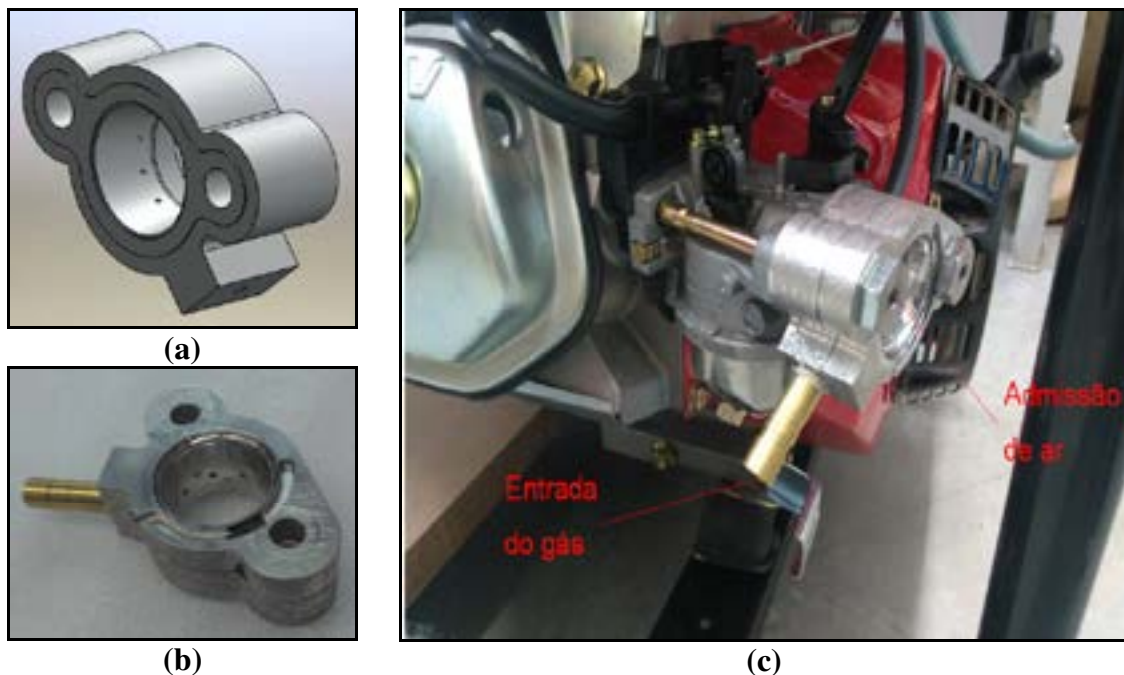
Mesclador (Misturador Ar-Gás) – (a) Desenho esquemático – (b) Peça usinada – (c) Peça montada no Motor à Combustão
